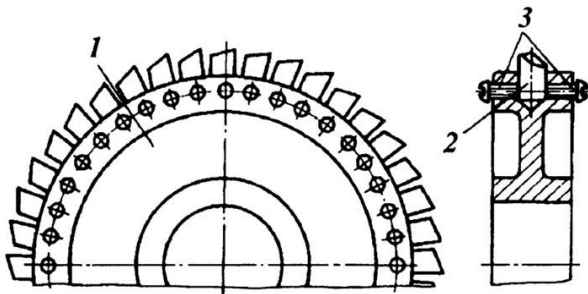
багатолезовий різальний інструмент для лезової обробки боропластику.
